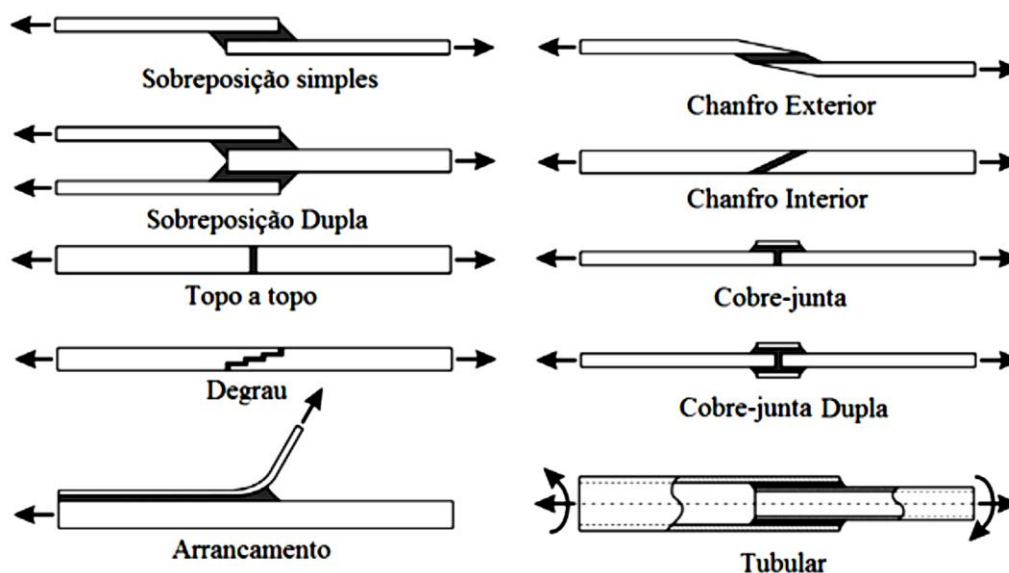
Tipos de configurações de juntas adesivas (da Silva et al. 2007).
